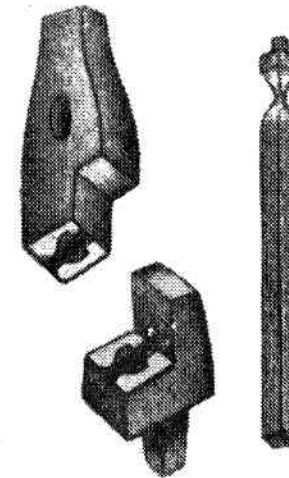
Ручной штампъ для штампованія винтовыхъ шиповъ.
